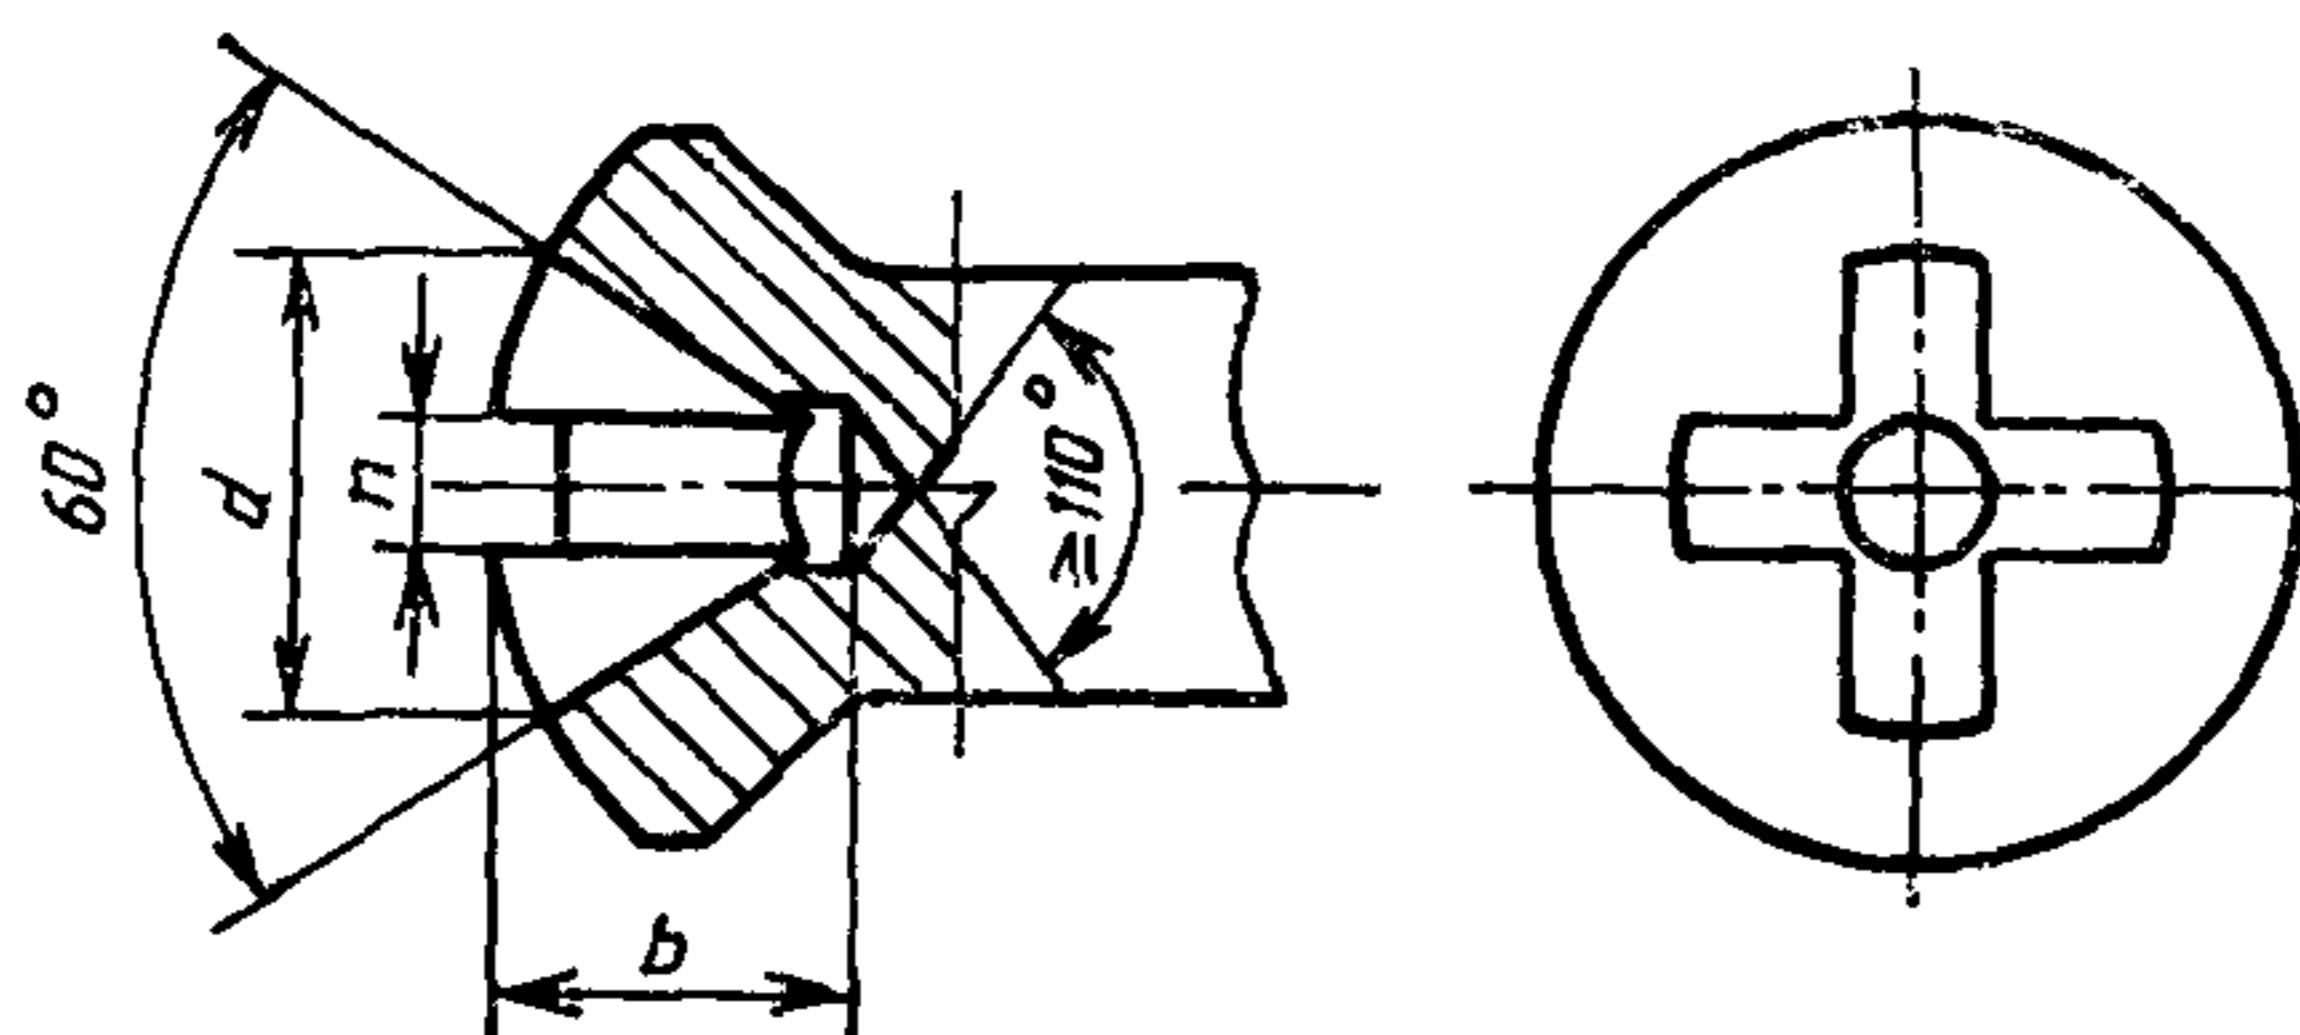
Головка с внутренним крестообразным шлицем
